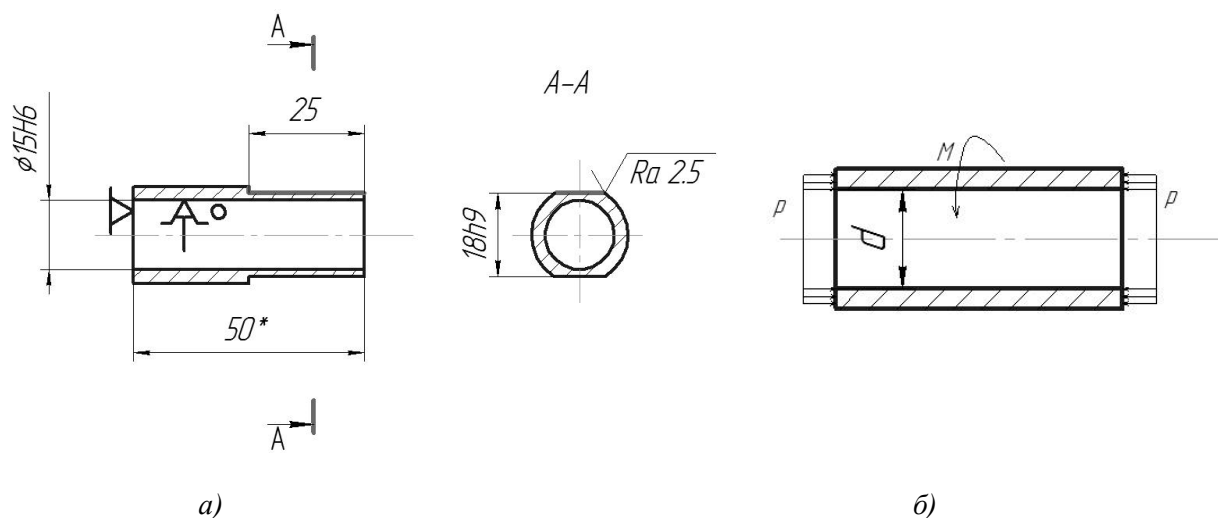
Установка заготовки в разжимной оправке с упором в торец:
